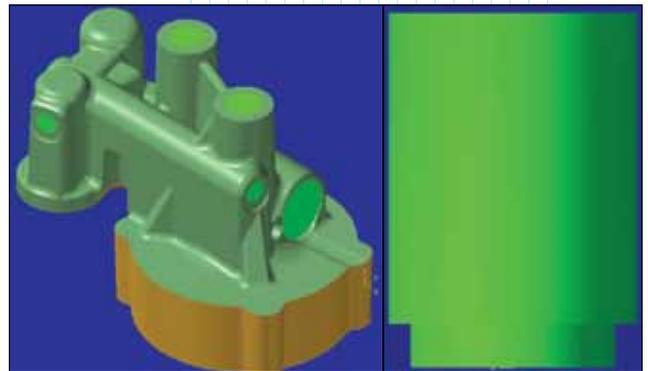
Модель детали, для обработки которой будет использоваться новая траектория "Динамическая дообработка"; справа – исходная заготовка
